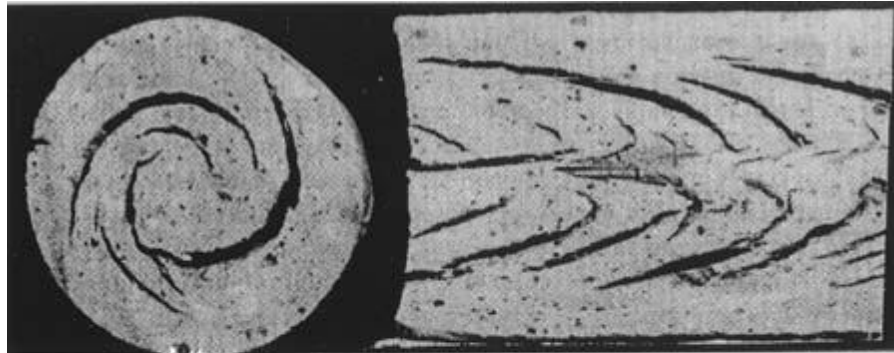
Defecto de piezas fabricadas mediante extrusión.
